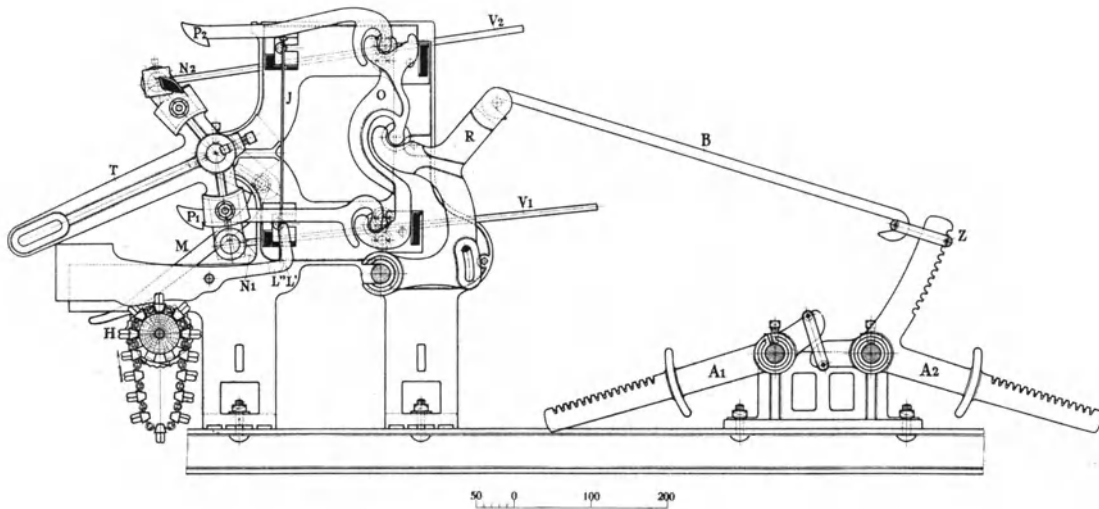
Schafmaschine von Stäubli mit Holzkarten und schwingbarem Messer.
